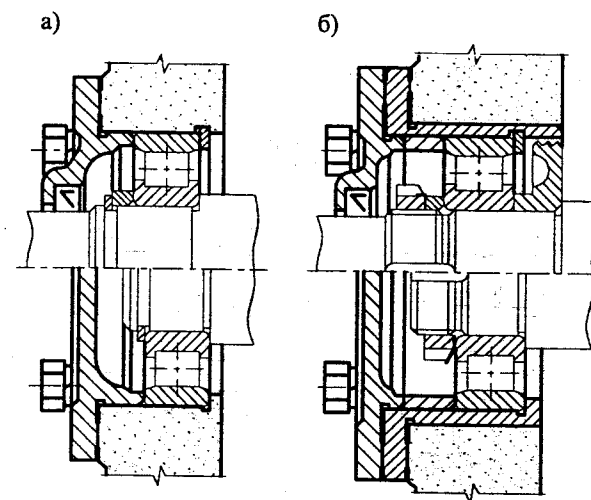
Установка наружного кольца разъемного подшипника в корпусе плавающей (самоустанавливающейся) опоры
